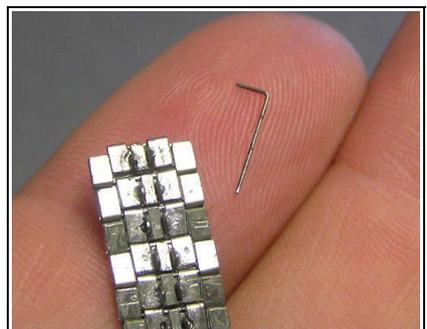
Die Kette wird mit einem, zum Haken gebogenen 0,3mm Stahlstift, geschlossen.
